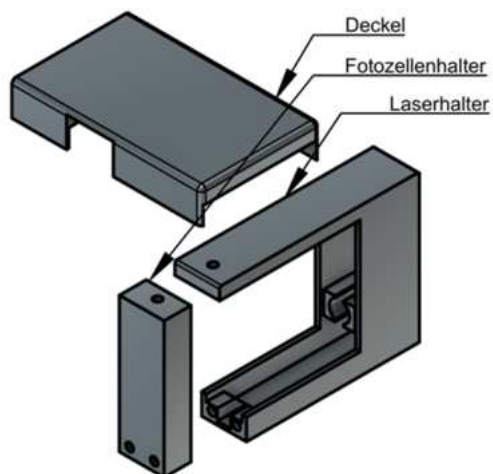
3D-gedruckte Lichtschrankenkomponenten
